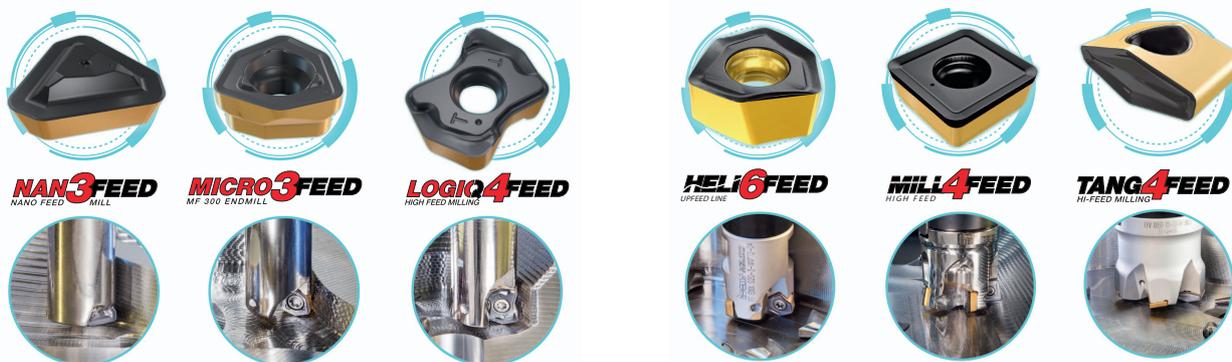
Линейки инструмента ISCAR для фрезерования с высокой подачей
